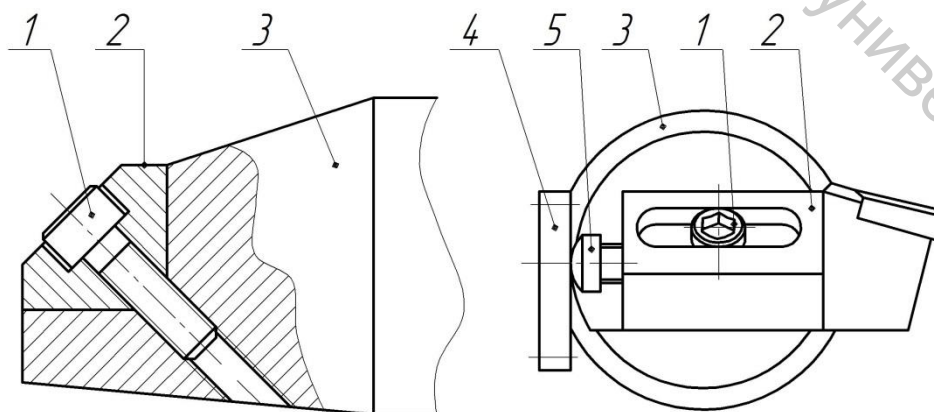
Резцовая вставка с расточной борштангой
